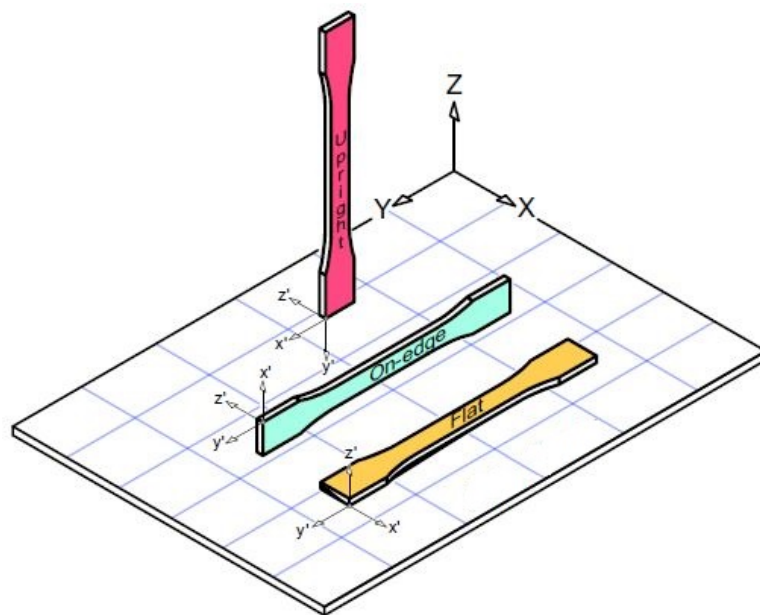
Orientação de construção para impressão 3D. Fonte: Adaptado de [Chacon et al. \(2017\)](#).
